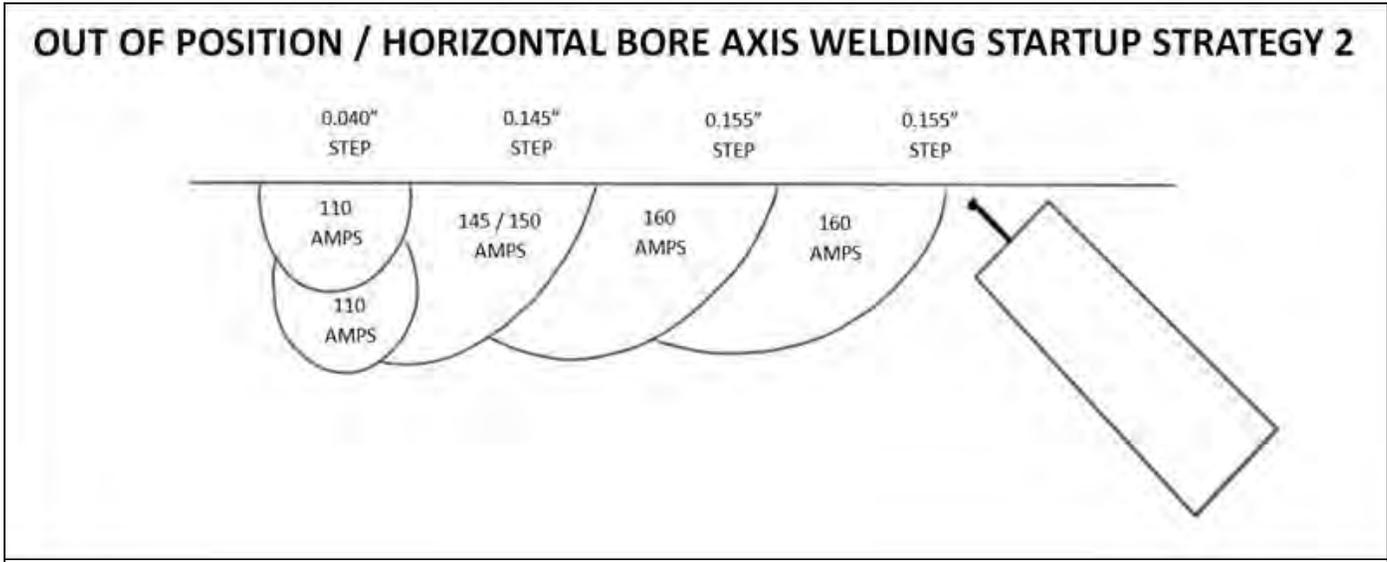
STRATÉGIE 2 POUR LE DÉMARRAGE DU SOUDAGE HORS POSITION/AXE D'ALÉSAGE HORIZONTAL
